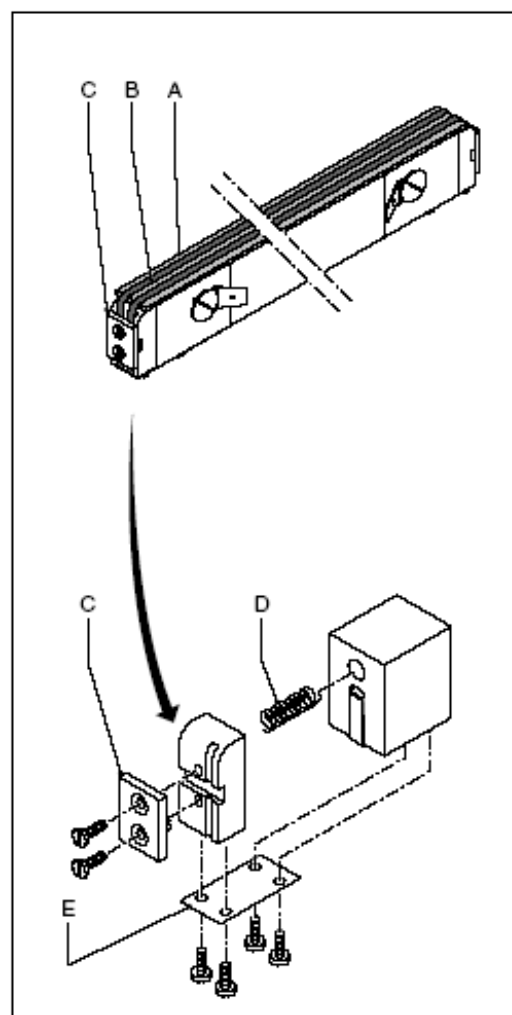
Cambio de alambres (máquinas con tapa de metal)
